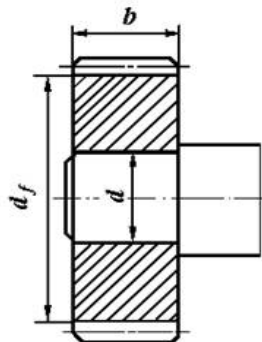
Цилиндрическое соединение вала и шестерни с натягом
